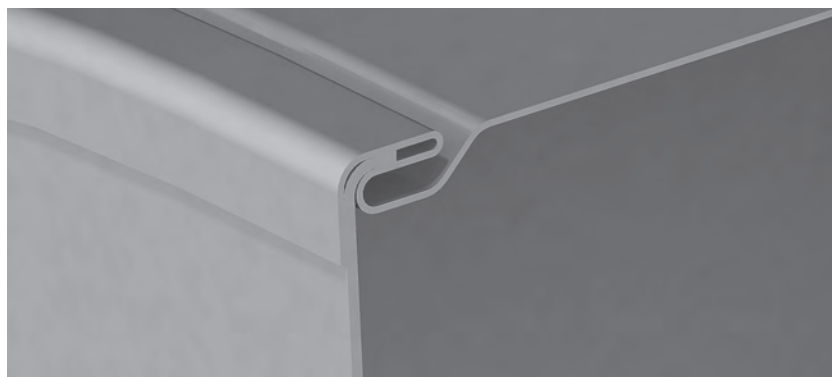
Сборка корпуса вентилятора на питтсбургском фальце
